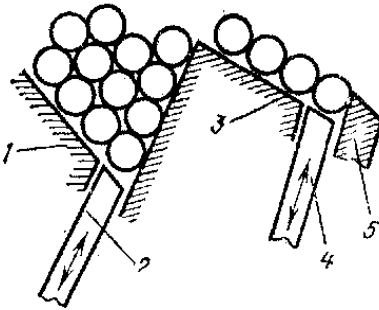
Схема бункерного пристрою з захватним механізмом
